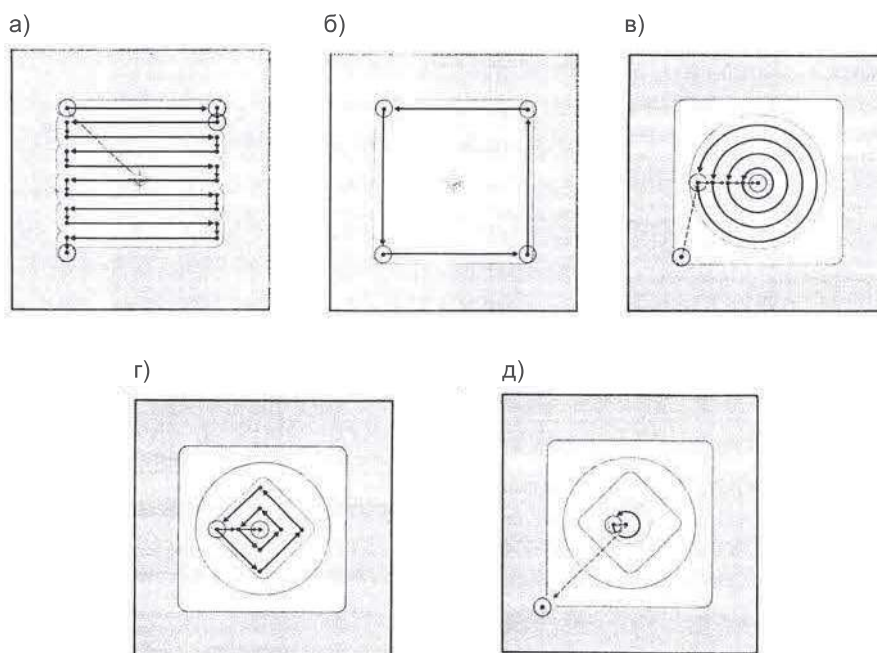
Схемы фрезерования внутреннего контура детали пальцевой фрезой: а) построчное фрезерование; б) фрезерование контура квадрата, в) построчное, круговое фрезерование плоскости круга, г) фрезерование плоскости квадрата, д) фрезерование плоскости и контура диаметром 10 мм
